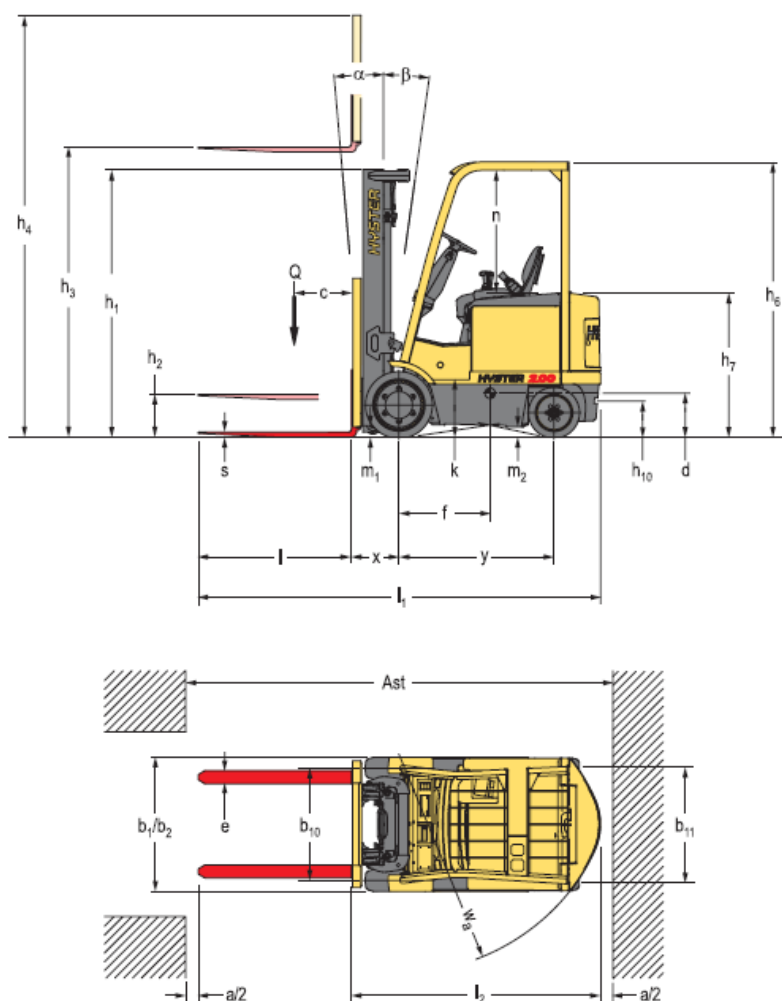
137: Dimensiones - Carretilla elevadora E 1,75 XM.
